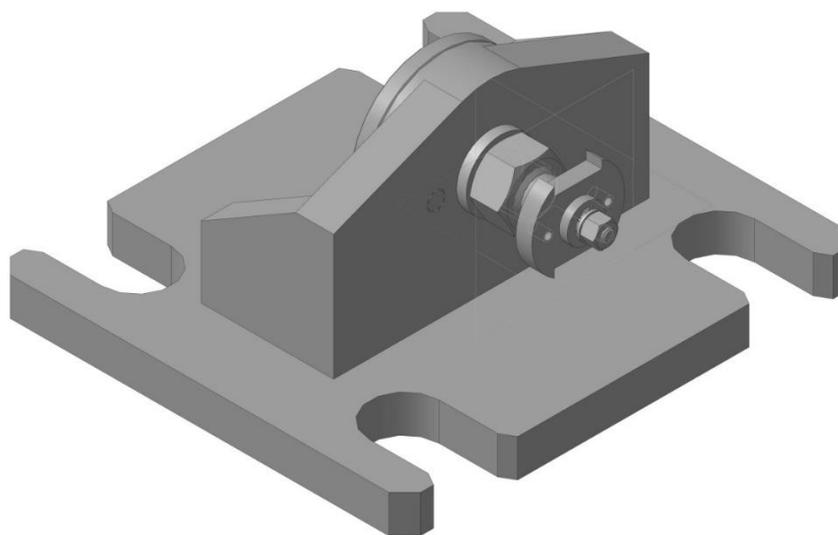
специальное станочное приспособление для фрезерной операции
